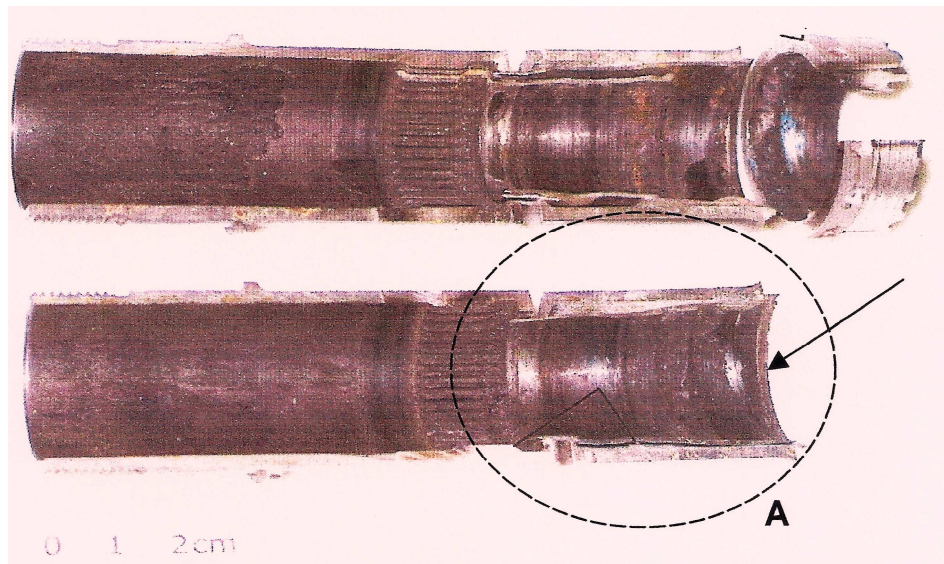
corte longitudinal do eixo externo, apresentando parte do eixo de N2 separado por fusão.
